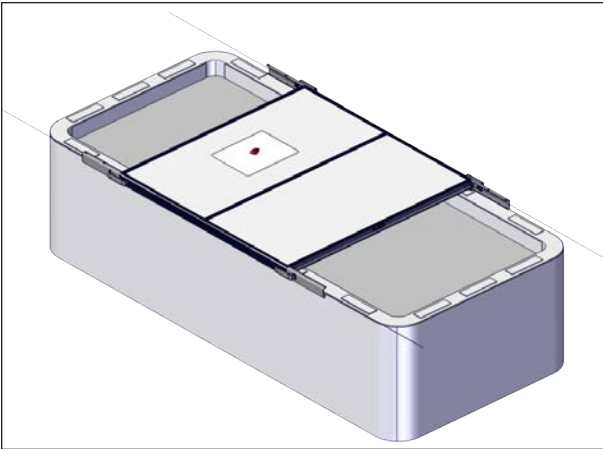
INSTALLATION DU COUVERCLE SUR LE SPA
